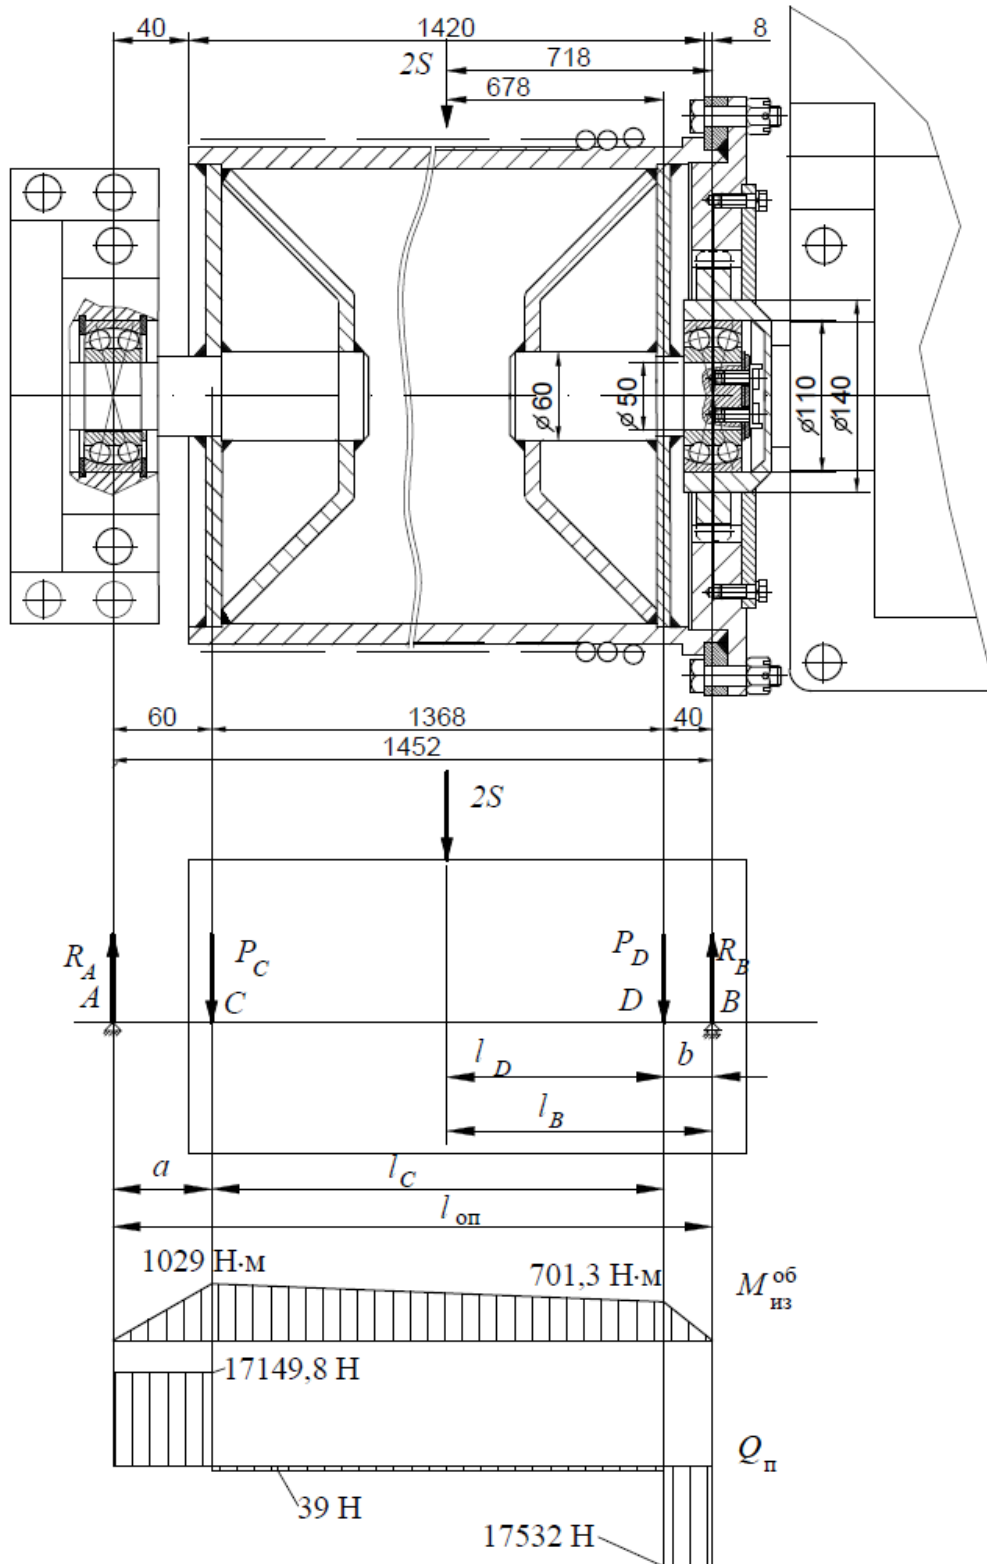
Схема к расчету оси (цапфы) барабана
